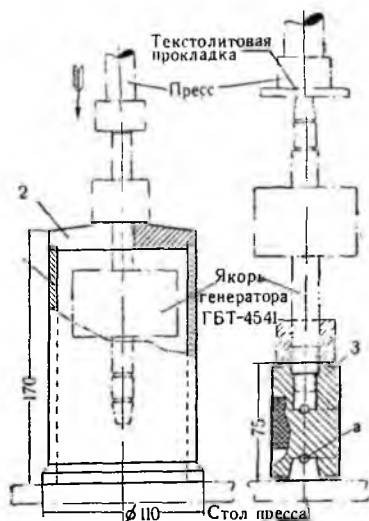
Приспособления для запрессовки и выпрессовки коллекторов.
